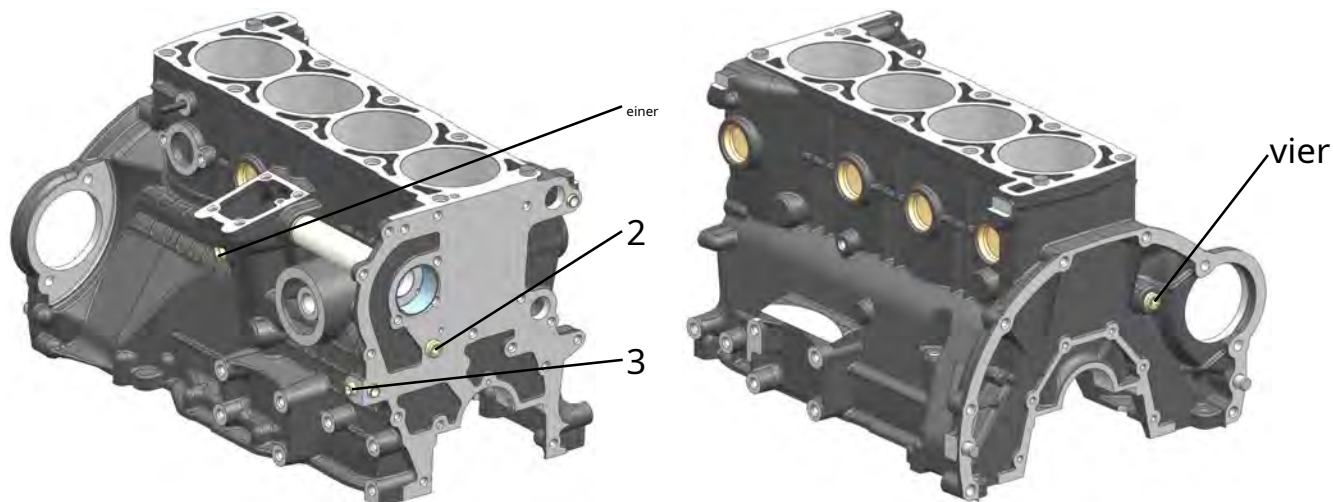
Ölkanalstopfen des Zylinderblocks:
